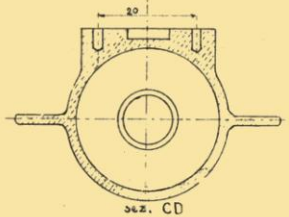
Sezione secondo un piano passante per C-D (v. fig. 8)
